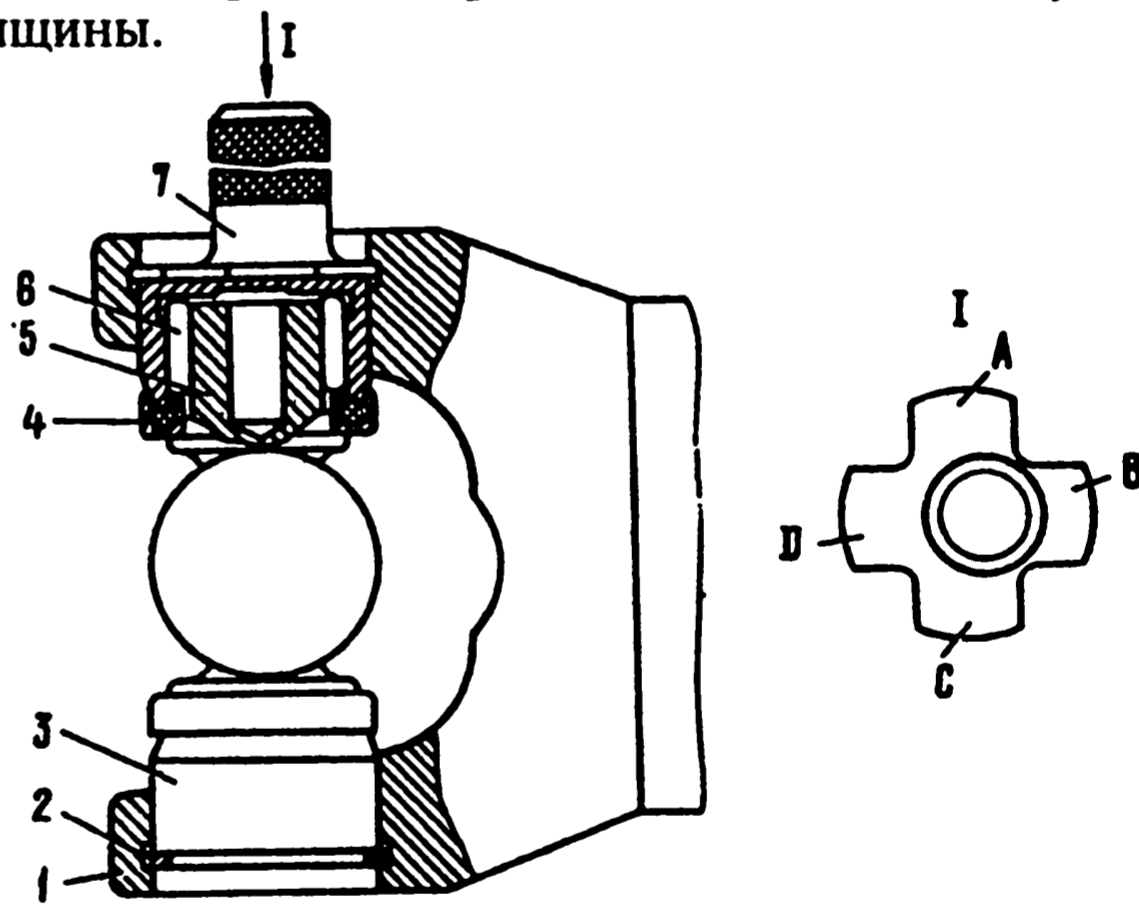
Сборка карданного шарнира: 1 - вилка карданного шарнира; 2 - стопорное кольцо; 3 - корпус подшипника; 4 - сальник; 5 - шип крестовины; 6 - игла подшипника; 7 - калибр 41.8734.4092. А, В, С, D лепестки калибра, имеющие толщину 1,53; 1,56; 1,59; 1,62 мм
